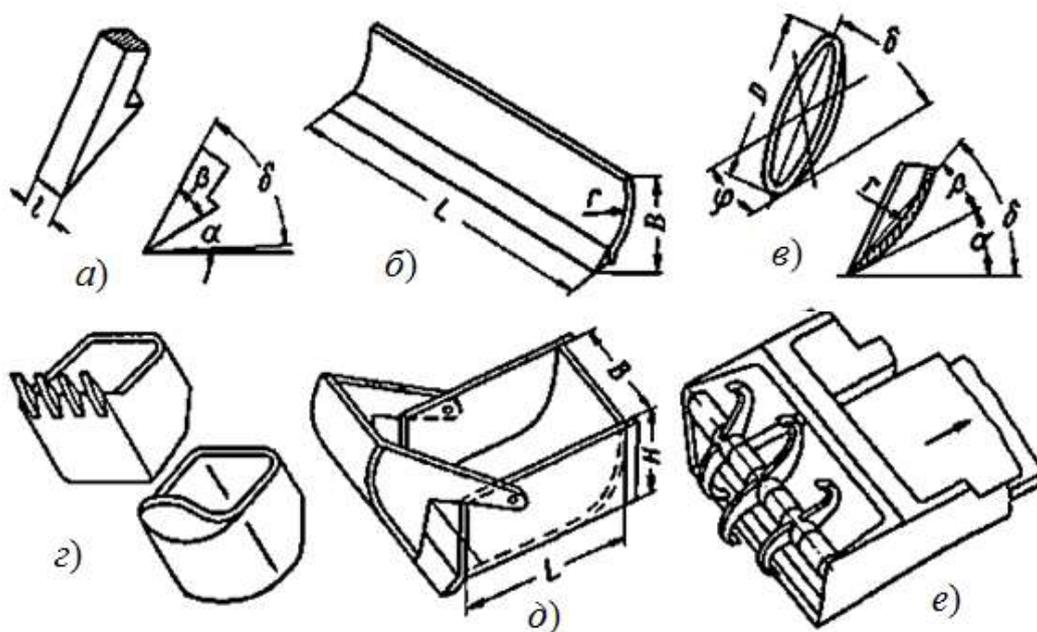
Рабочие органы землеройных машин: *a* - зуб; *б* - отвал с режущим ножом; *в* - дисковый нож; *г* - ковш экскаватора с зубьями и ковш экскаватора с полукруглой режущей кромкой; *д* - ковш скрепера; *е* - рабочий орган землеройной машины с роторным рыхлителем.
